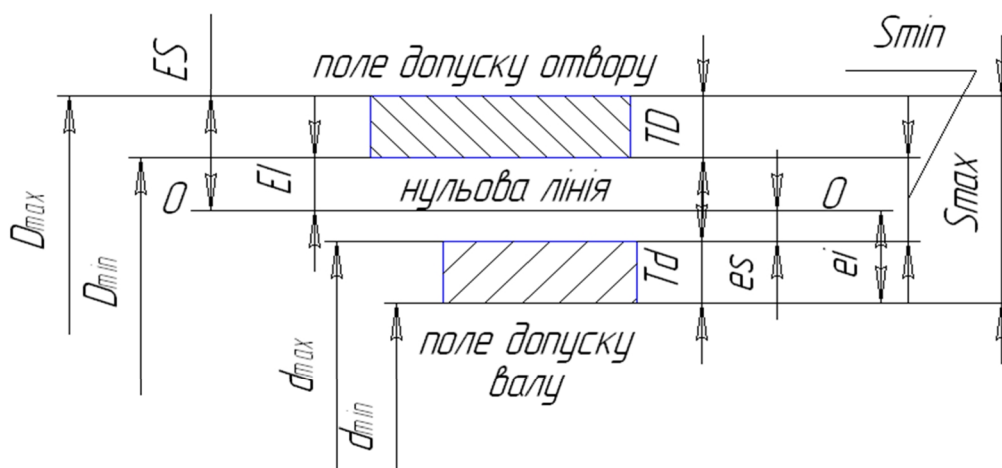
Схема полів допусків валу і отвору для посадок з зазором
